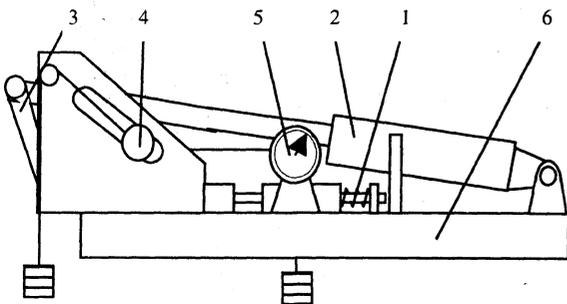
Устройство для торцево-прессовой деформации древесных заготовок
